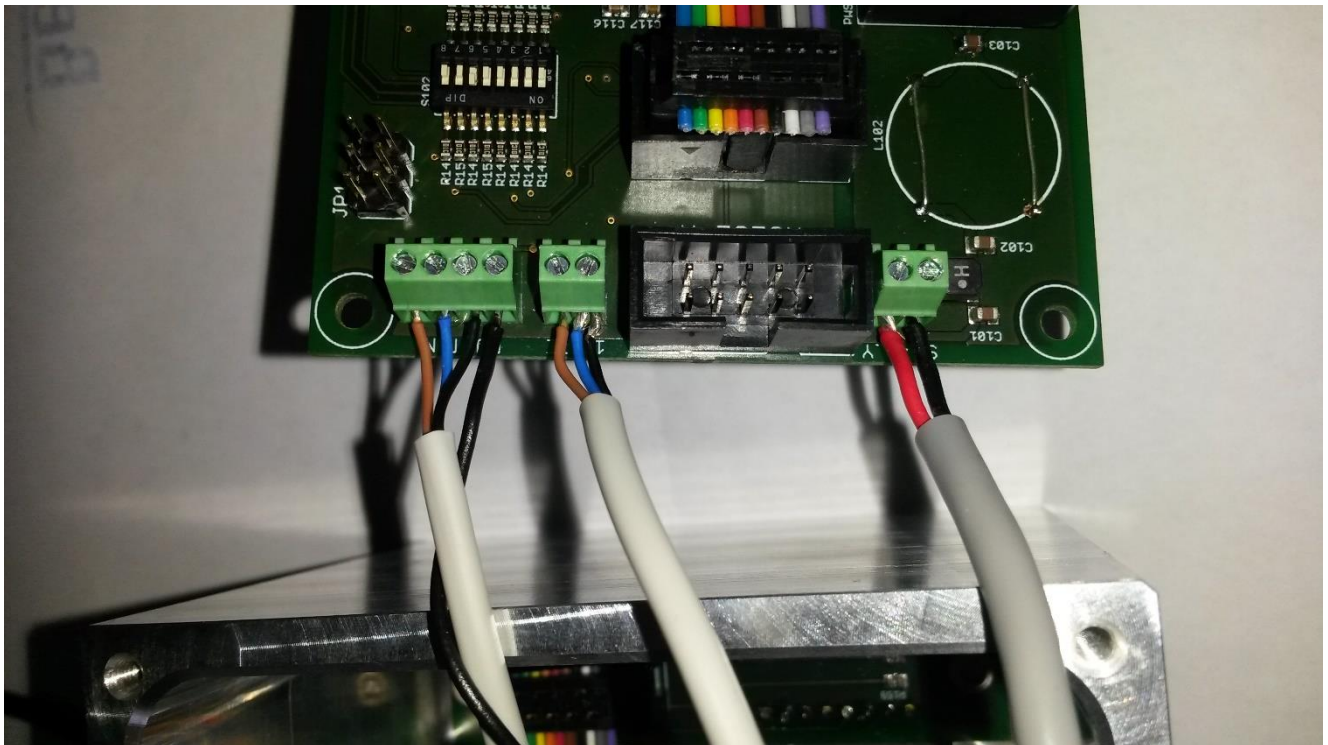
Verbindungskabel PCB zu Status-LED-PCB
